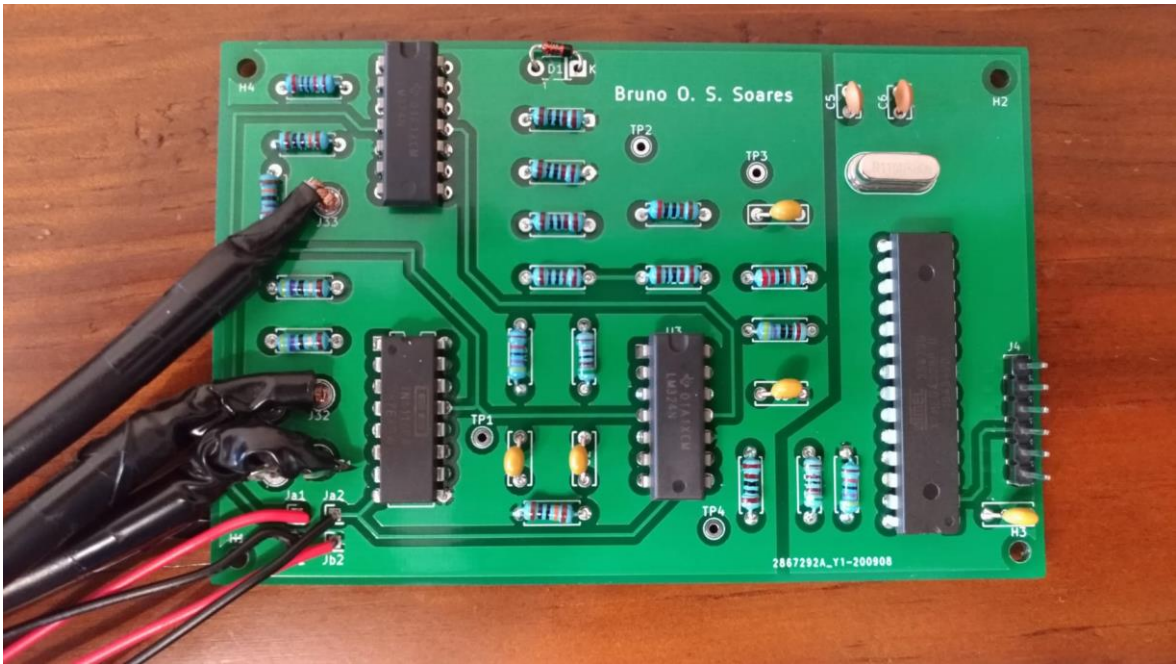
Placa de circuito impresso com componentes soldados.
